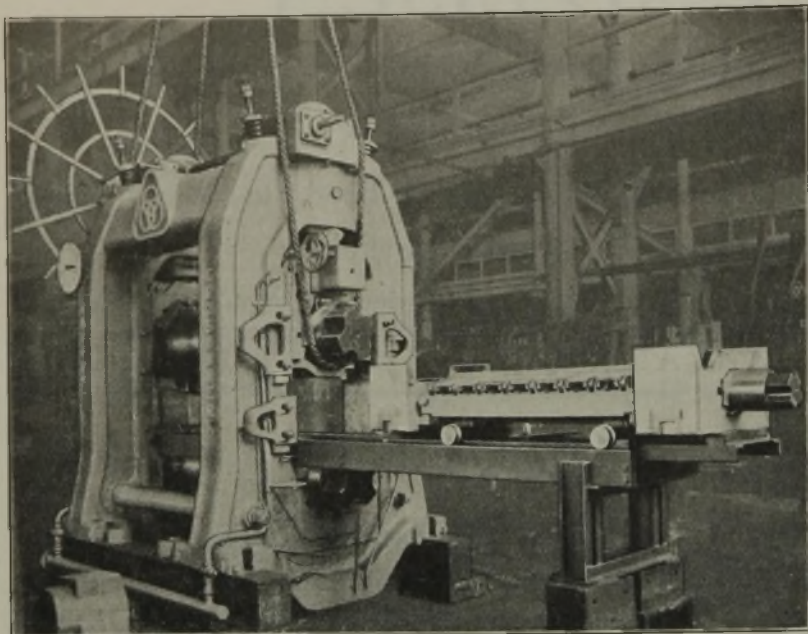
Ausbau der Mittelwalze zusammen mit Einbaustücken und Walzarmatur.
